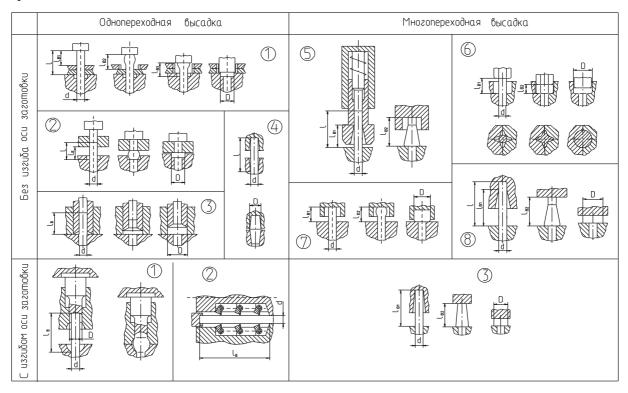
Устройства и способы высадки поковок с большим набором металла
